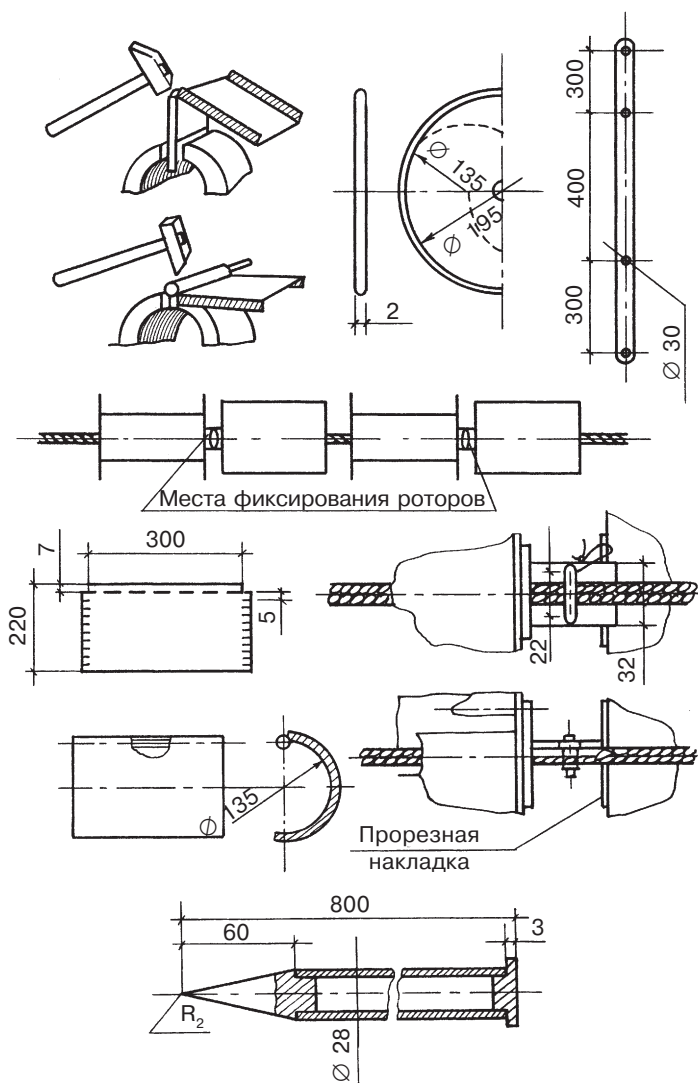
Чертежи для изготовления деталей и узлов двигателя для мини-ГЭС
